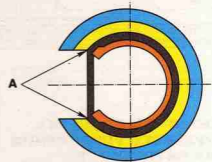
Установка опорной втулки рейки: А — места разреза уплотнительного кольца после установки втулки в картер рулевого механизма.
